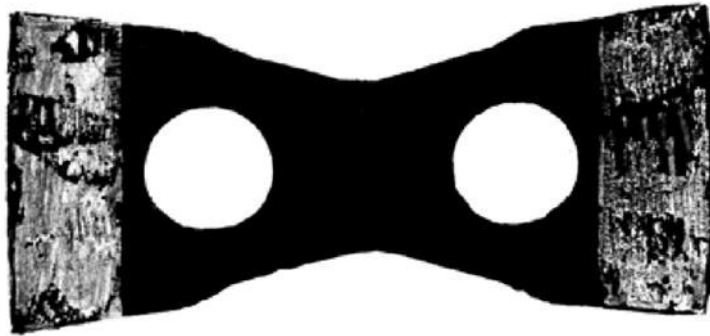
Изношенный молоток кормодробилки из стали 65Г после плазменного напыления
